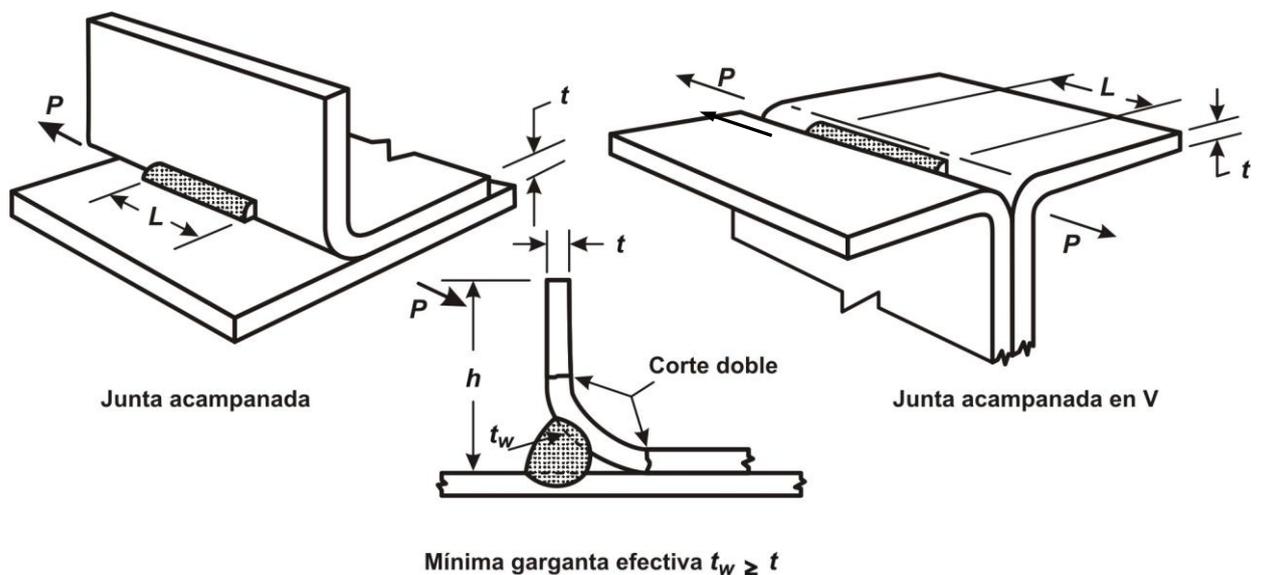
c.) Acciones de corte doble en uniones soldadas con juntas acampanadas.
